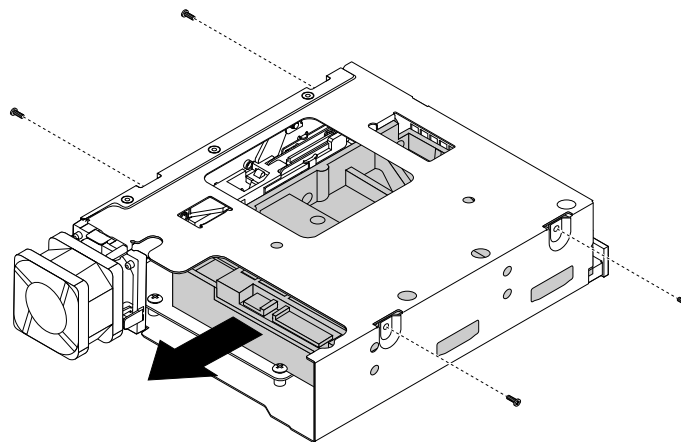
Festplattenlaufwerk auf der Halterung entfernen
